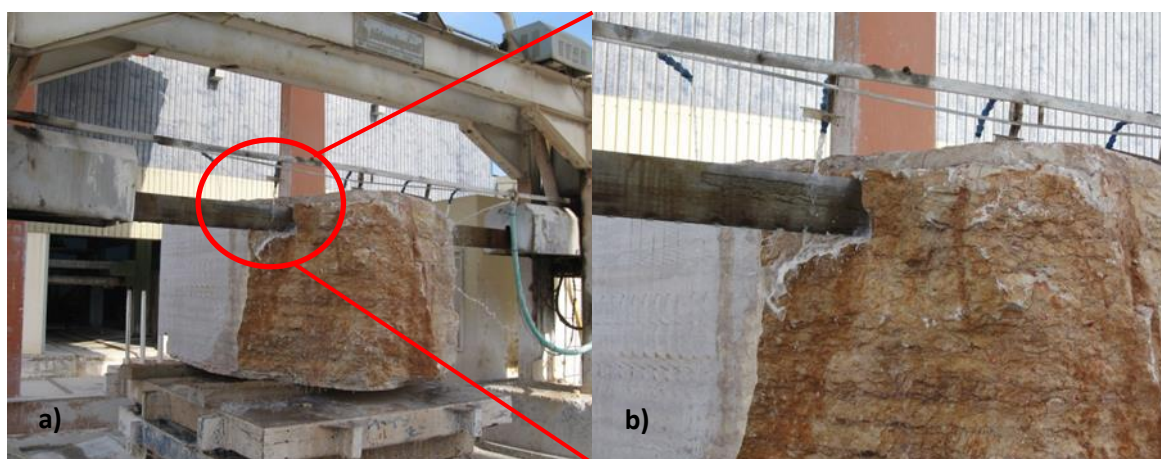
Pré-corte, vista geral a) e pormenor b).
